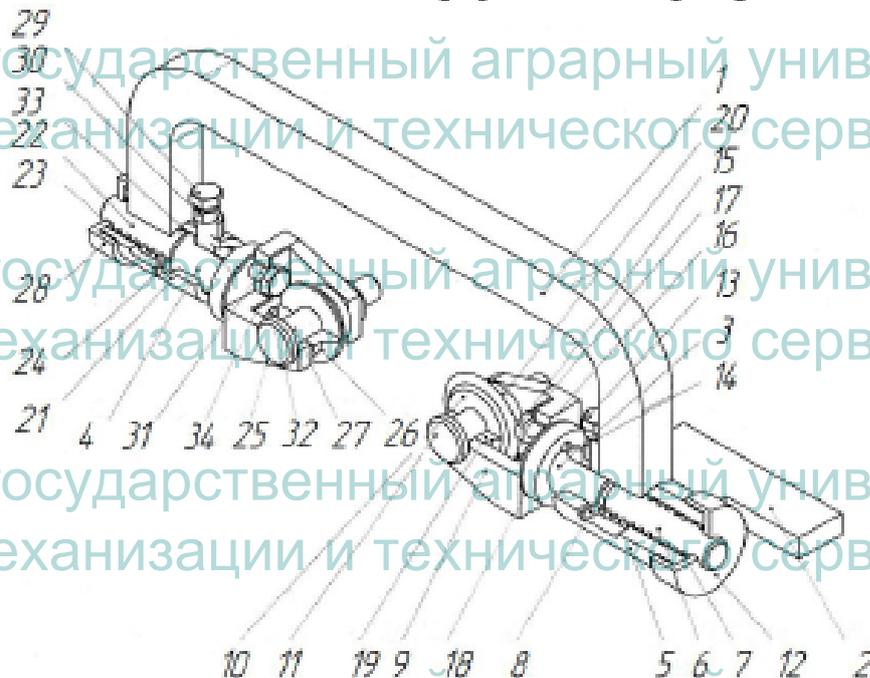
Устройство для упрочнения (АС № 2014100945/02)
